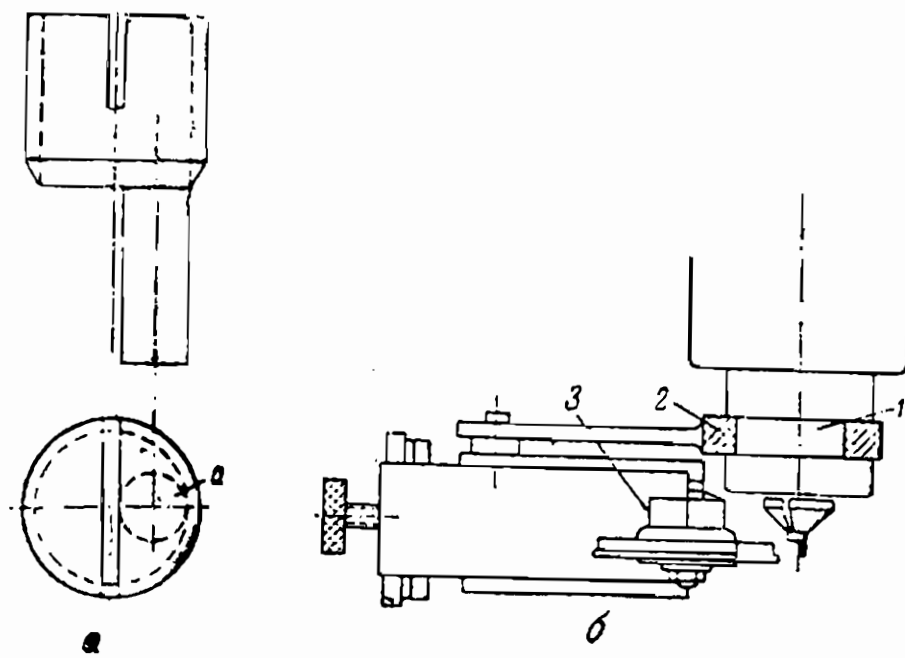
Схема патрона для обтачивания деталей с различными эксцентриситетами.
